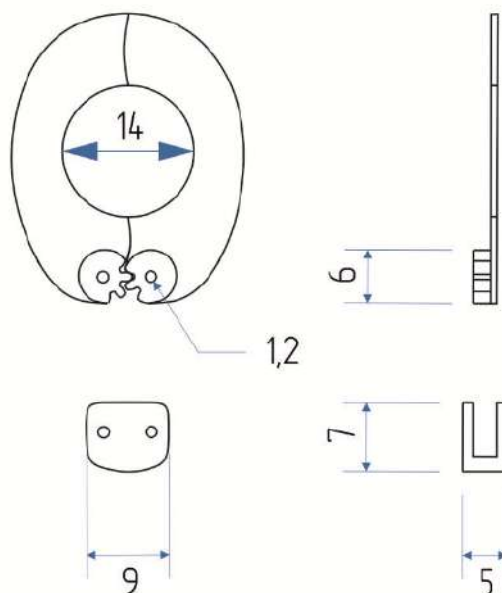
Чертеж механизма кольца для преобразования внешнего вида
